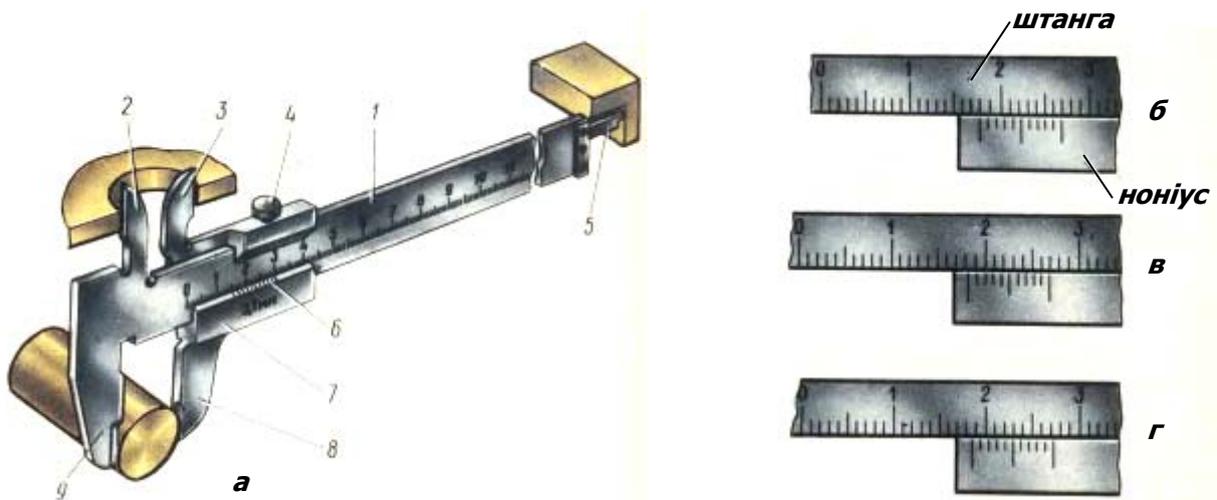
Вимірювання розмірів деталі штангенциркулем
